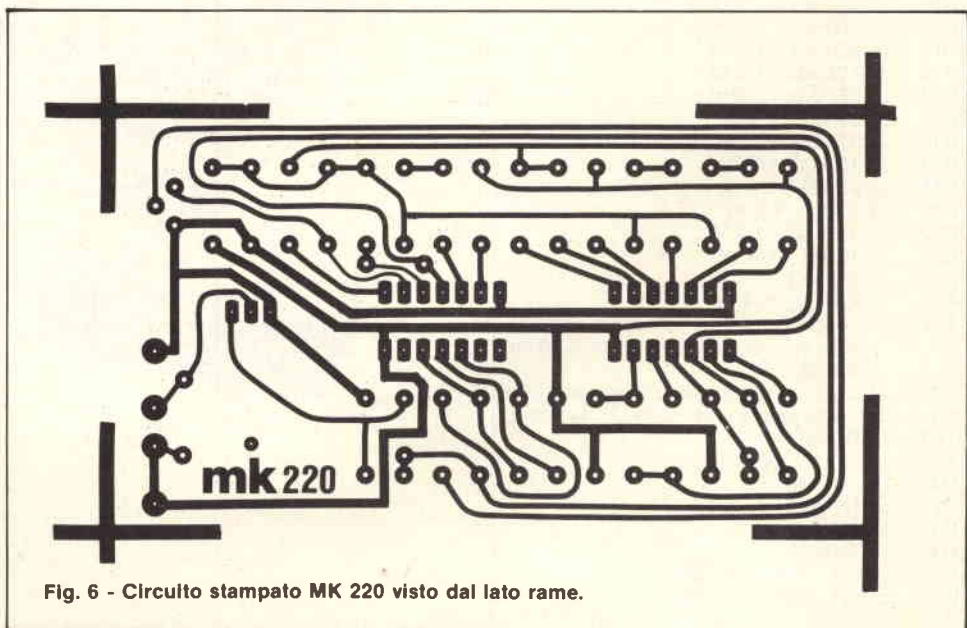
Circuito stampato MK 220 visto dal lato rame.
